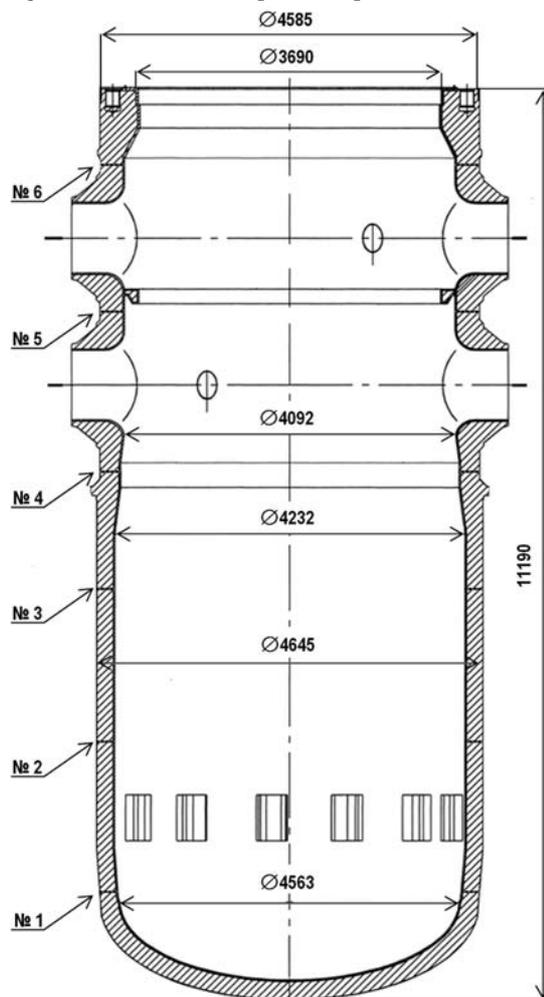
Схема расположения сварных соединений на корпусе ВВЭР-1200
